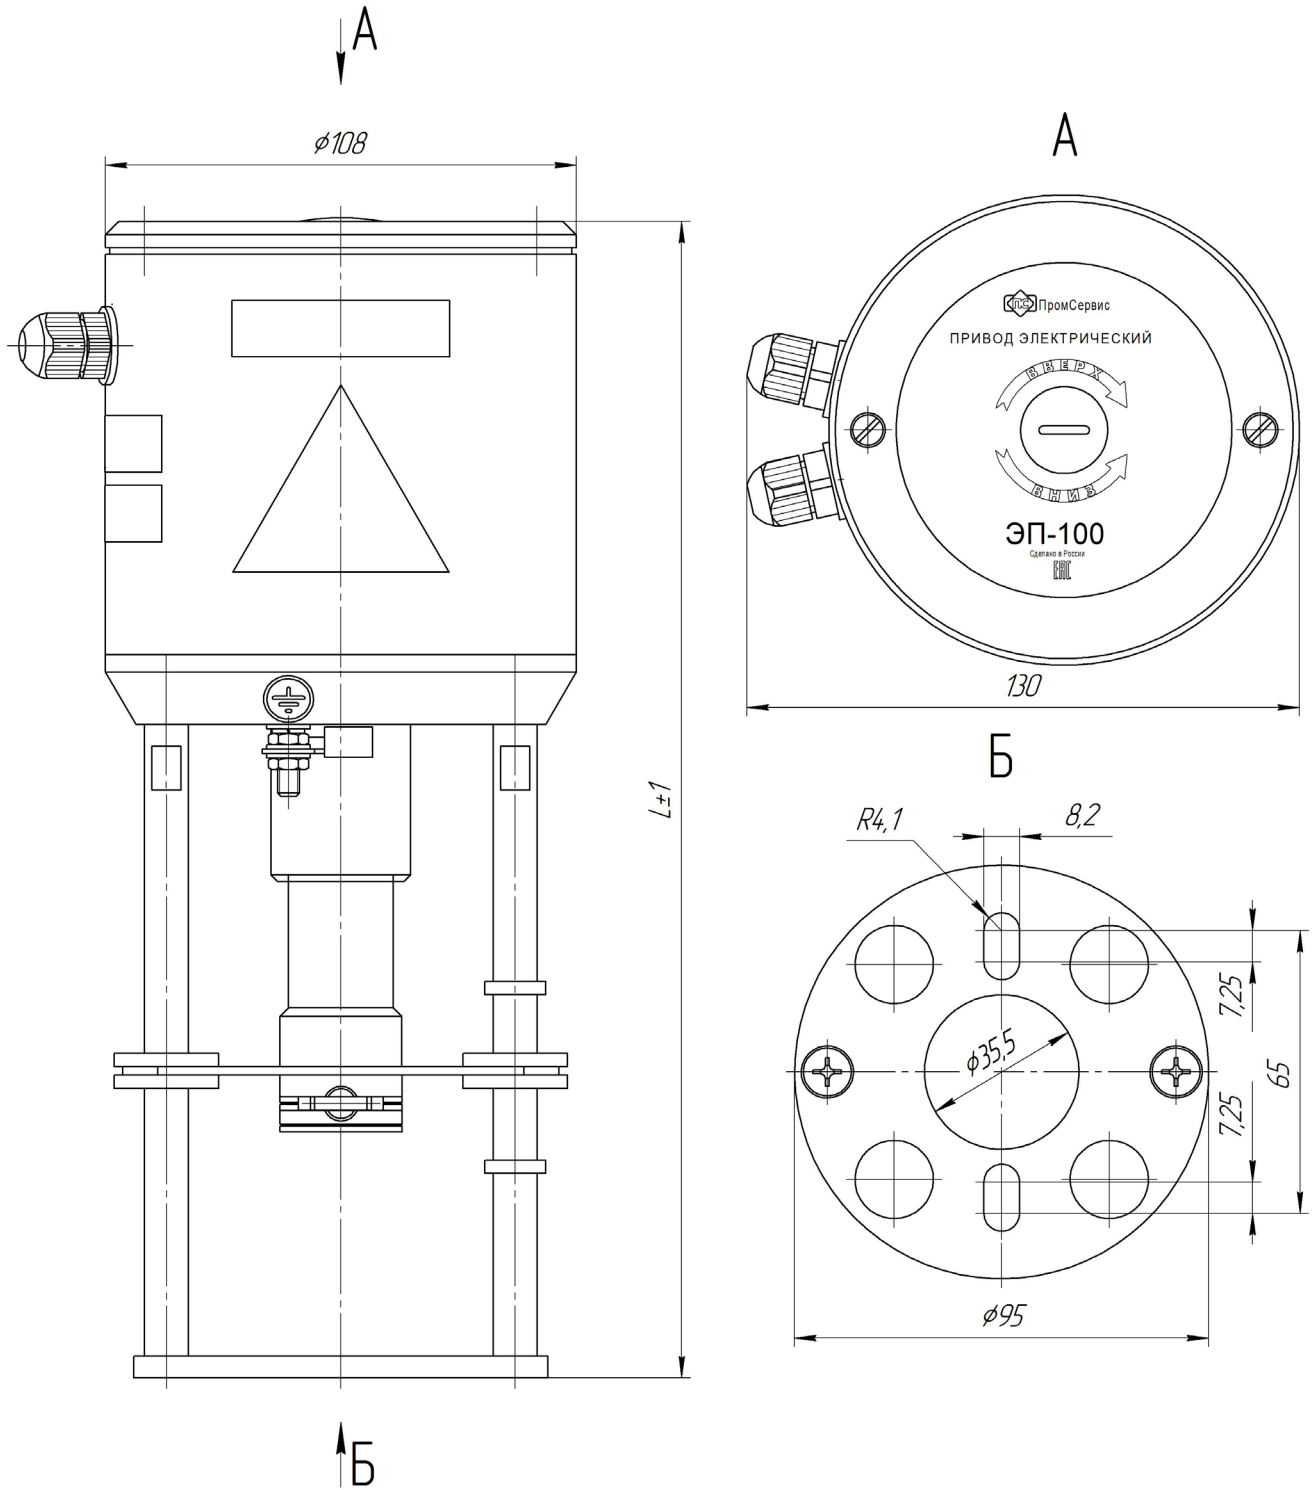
Габаритные и присоединительные размеры привода исполнения ЭП-100-05
